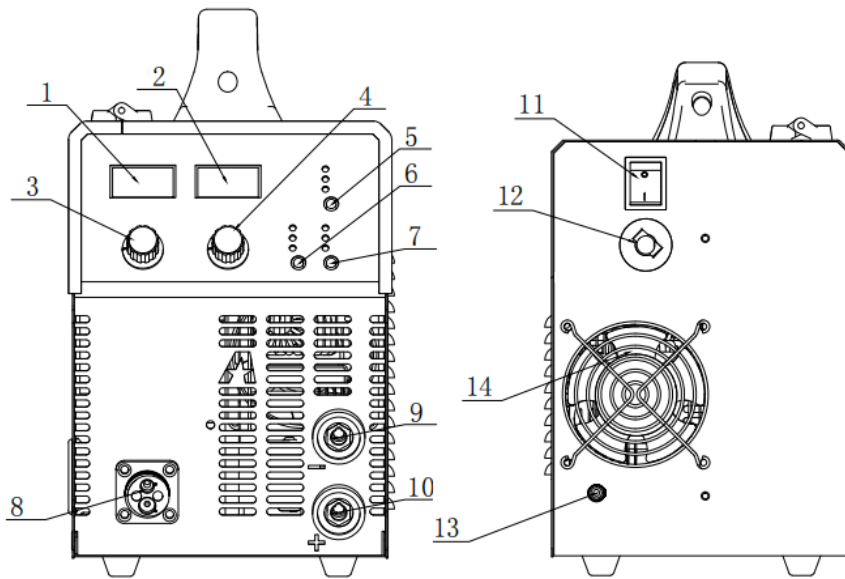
Общий вид (Инверторный сварочный полуавтомат)
